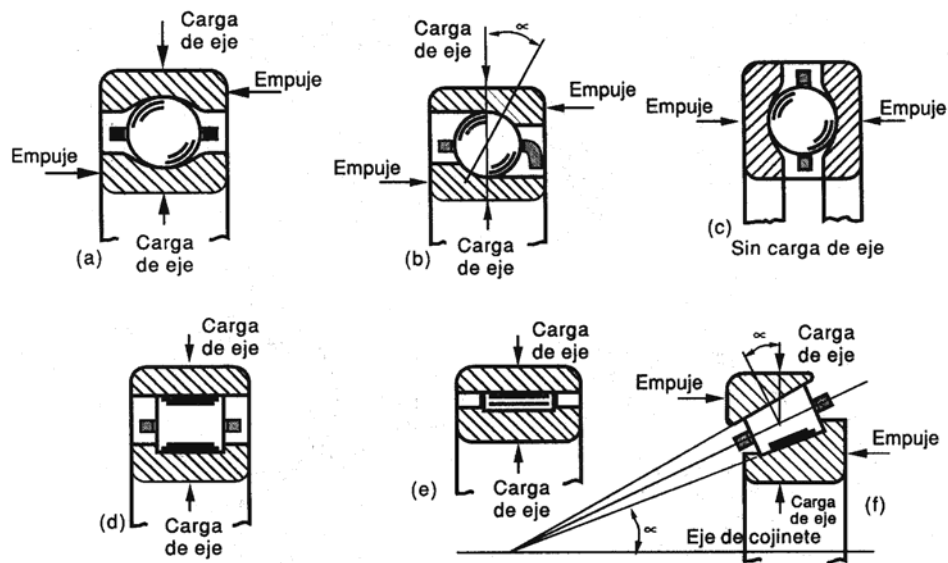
Tipos básicos de cojinetes de rodillos. A) cojinete de bolas de una hilera, b) cojinete de contacto angular, c) cojinete de empuje de una hilera, d) cojinete de rodillos cilíndricos, e) cojinete de rodillos de aguja, f) cojinete de rodillos cónicos.
